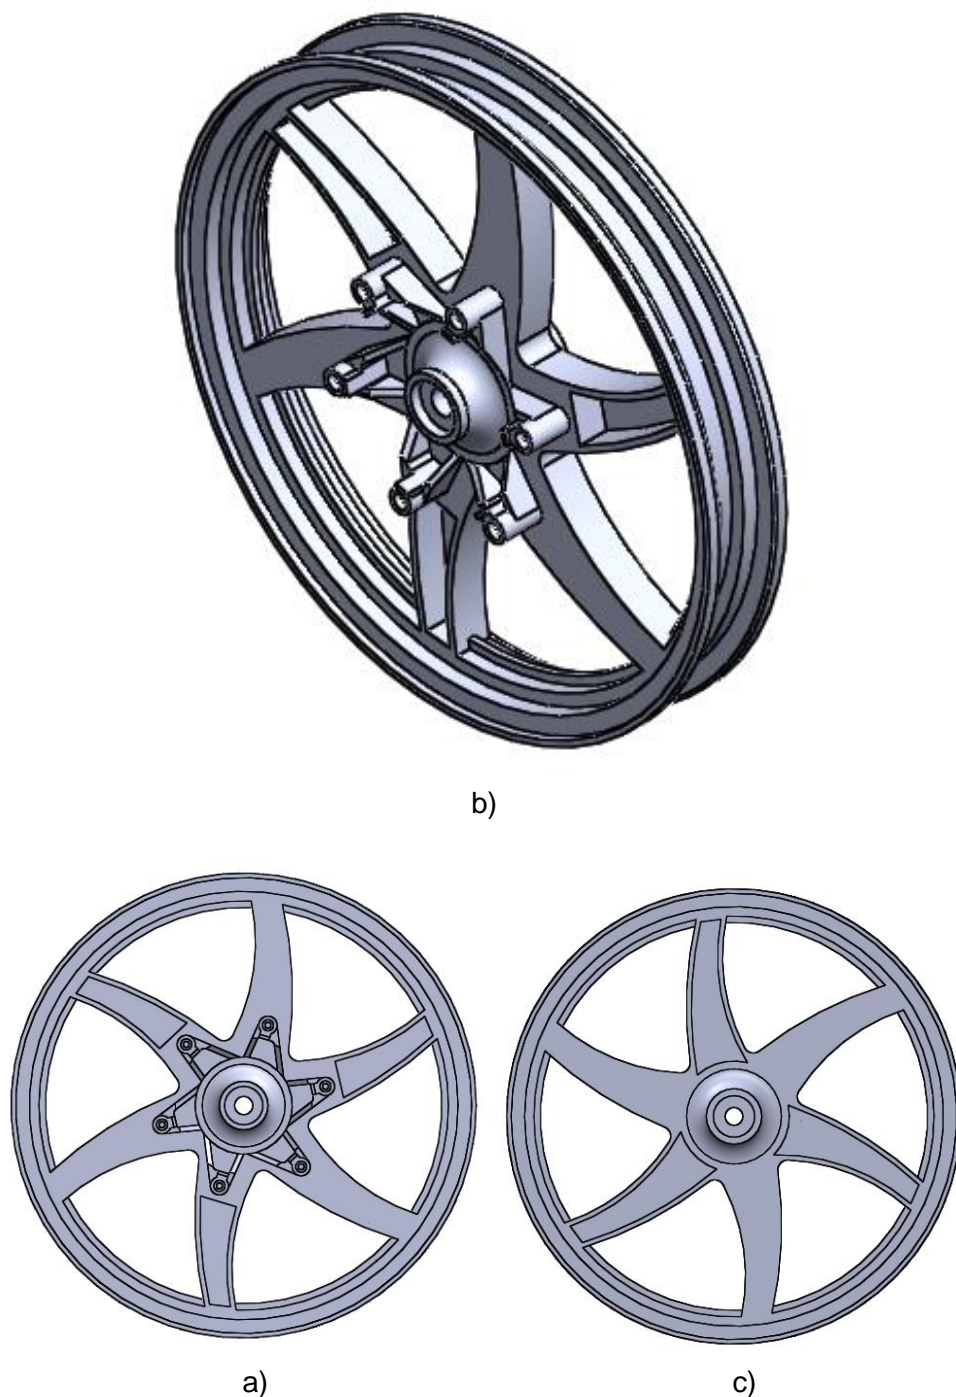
Diseño A.1 a) Vista frontal. b) Vista isométrica. c) Vista trasera. Fuente: Propia.
